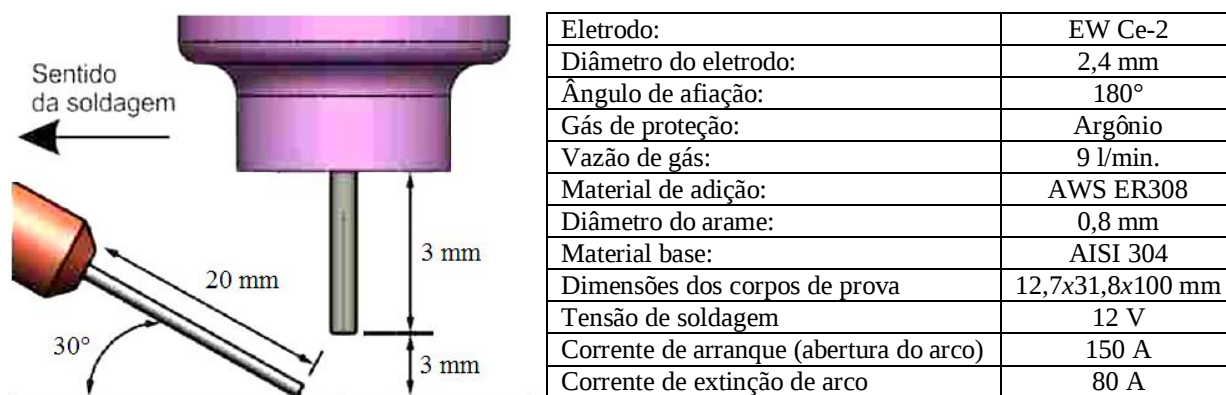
Parâmetros de soldagem empregados nos experimentos.
